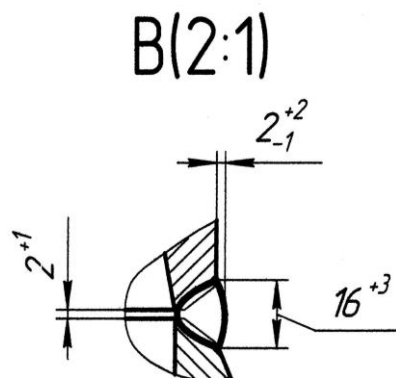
Геометрические параметры подготовки кромок под сварку бобышки 6 и штуцера резьбового 8 и параметры сварного соединения.
